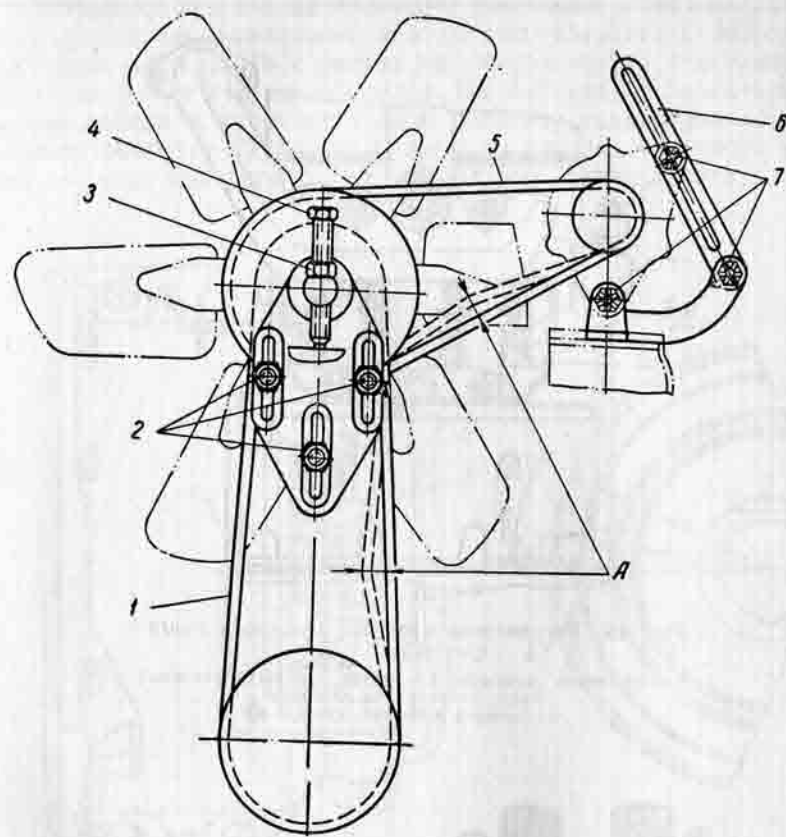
Проверка натяжения ремней вентилятора и генератора:
